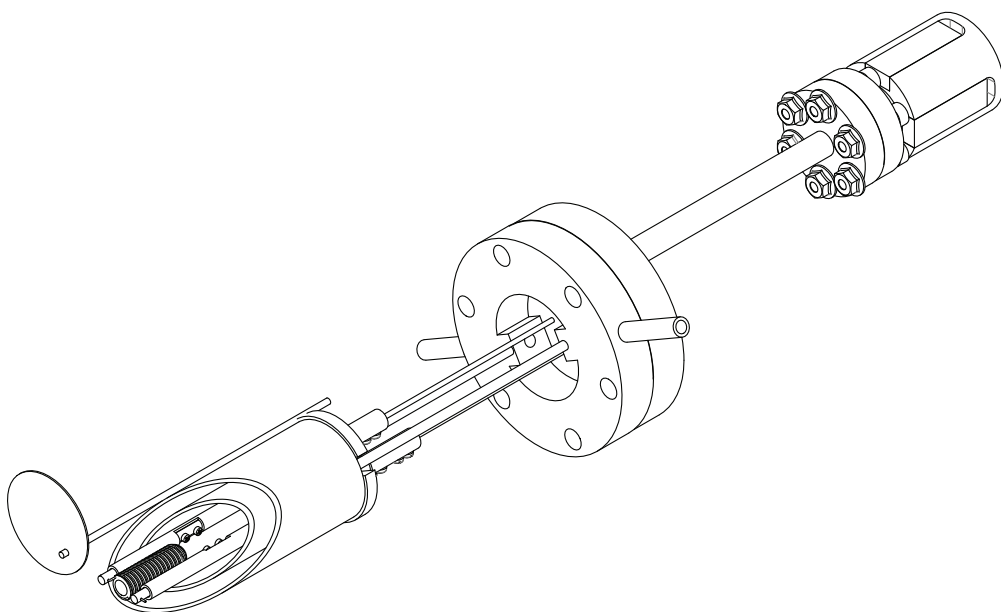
Evaporator for metal dosing - 1000도 이상의 고온에 사용할 수 있는 evaporator 디자인이다. 구조를 보기 편하게 water jacket는 잘라내었다. 뒤에 달려있는 CF1.33 파트는 rotation feedthrough로 flexible shaft(도면에 없음)를 사용해 shutter를 여닫을 수 있다.
